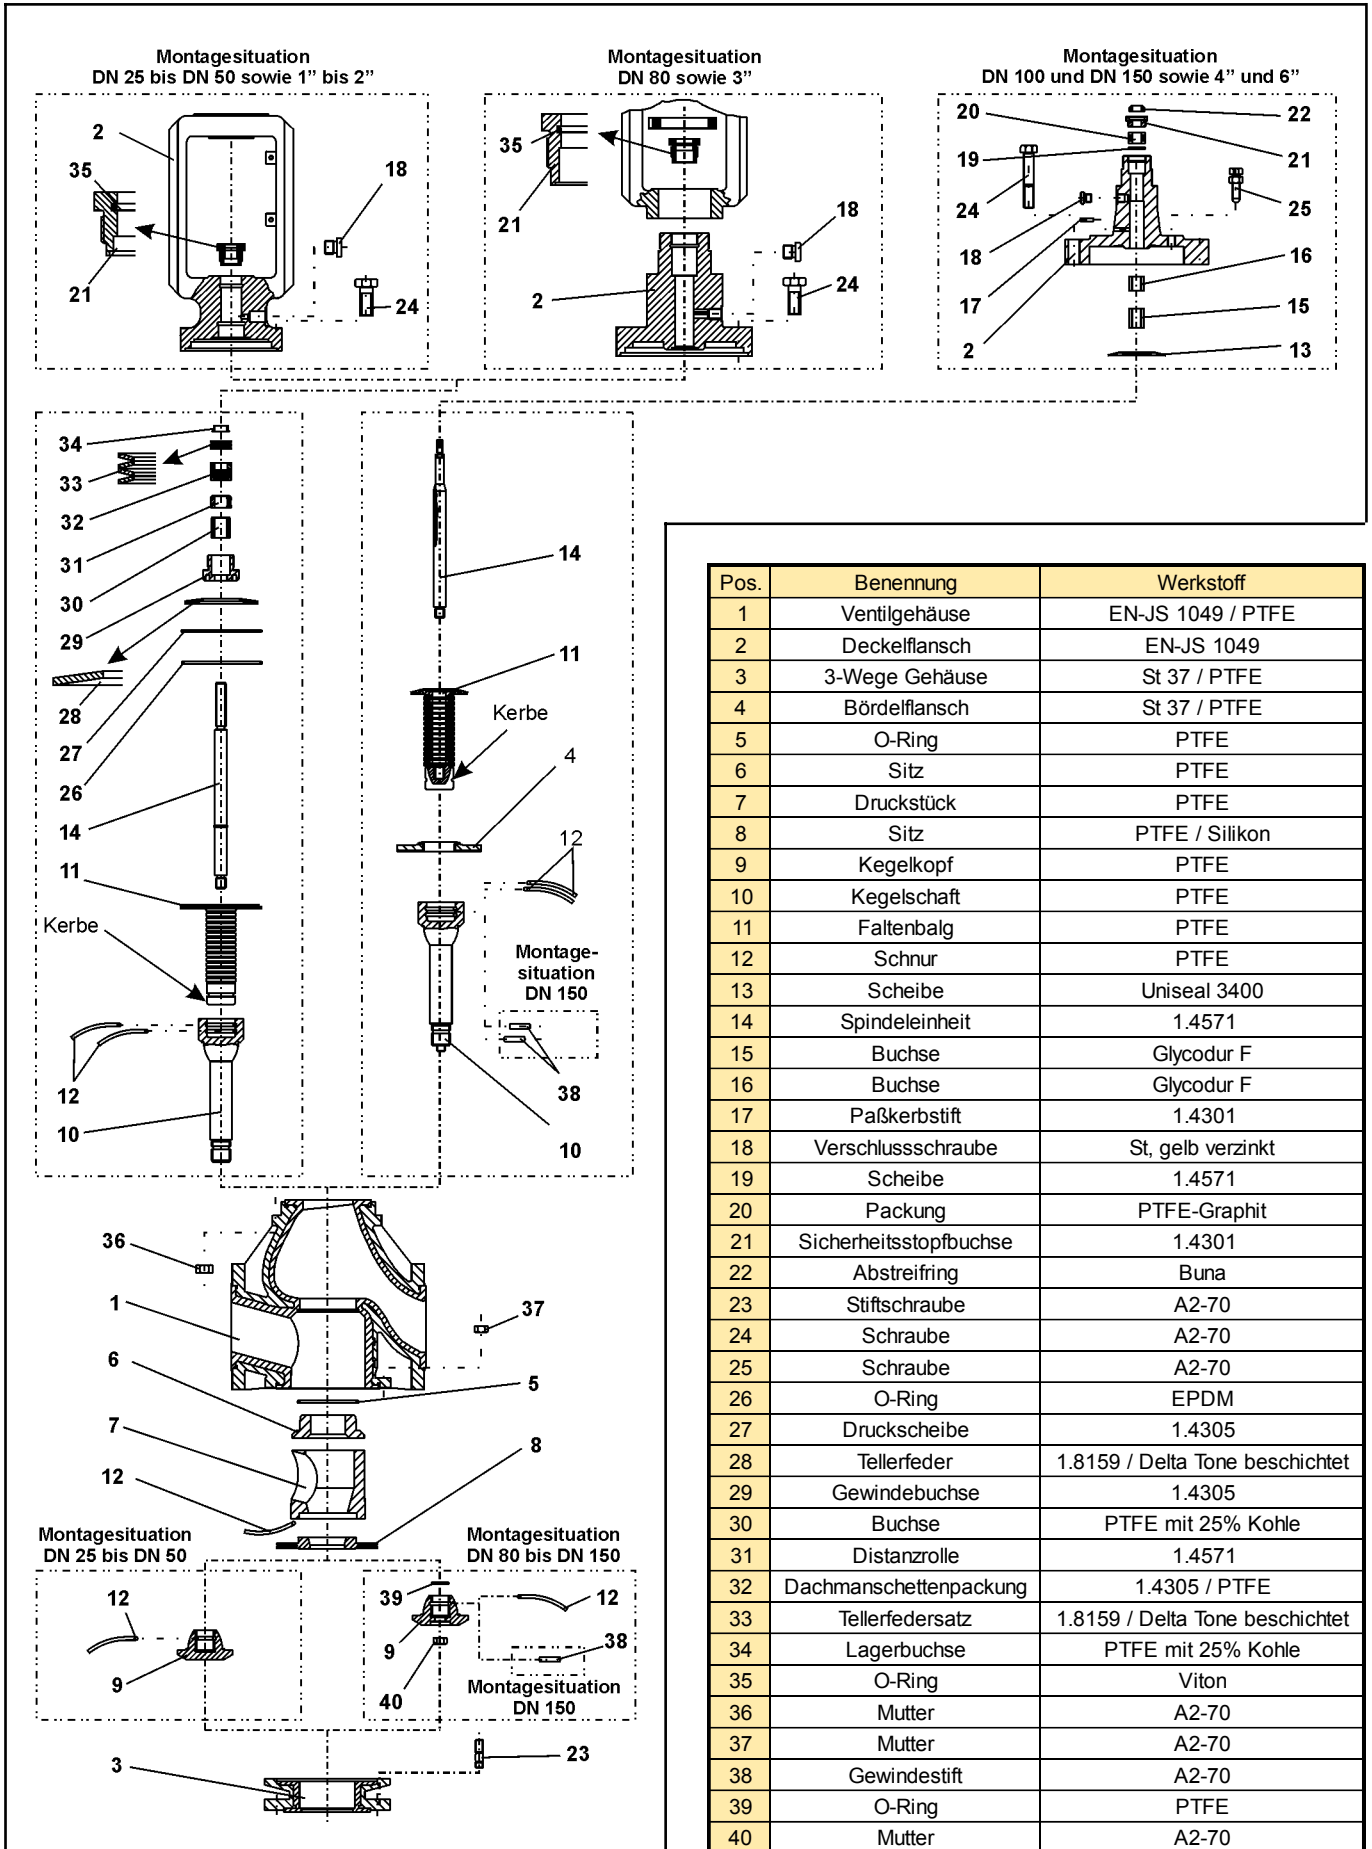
Explosionszeichnung des 3-Wege Ventils BR 1d
